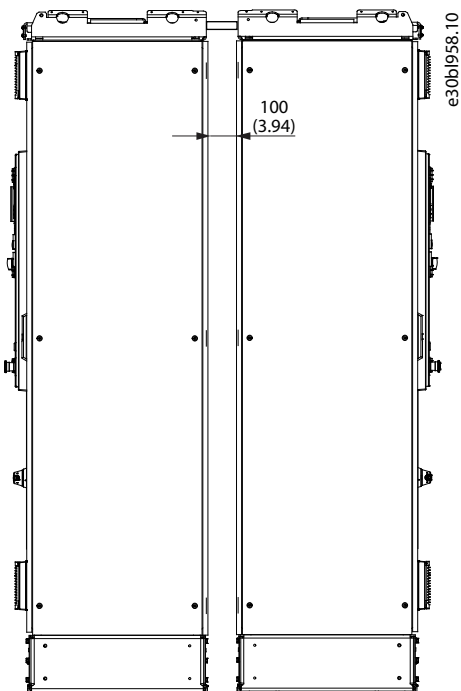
Installazione degli armadi back-to-back, mm (pollici)
